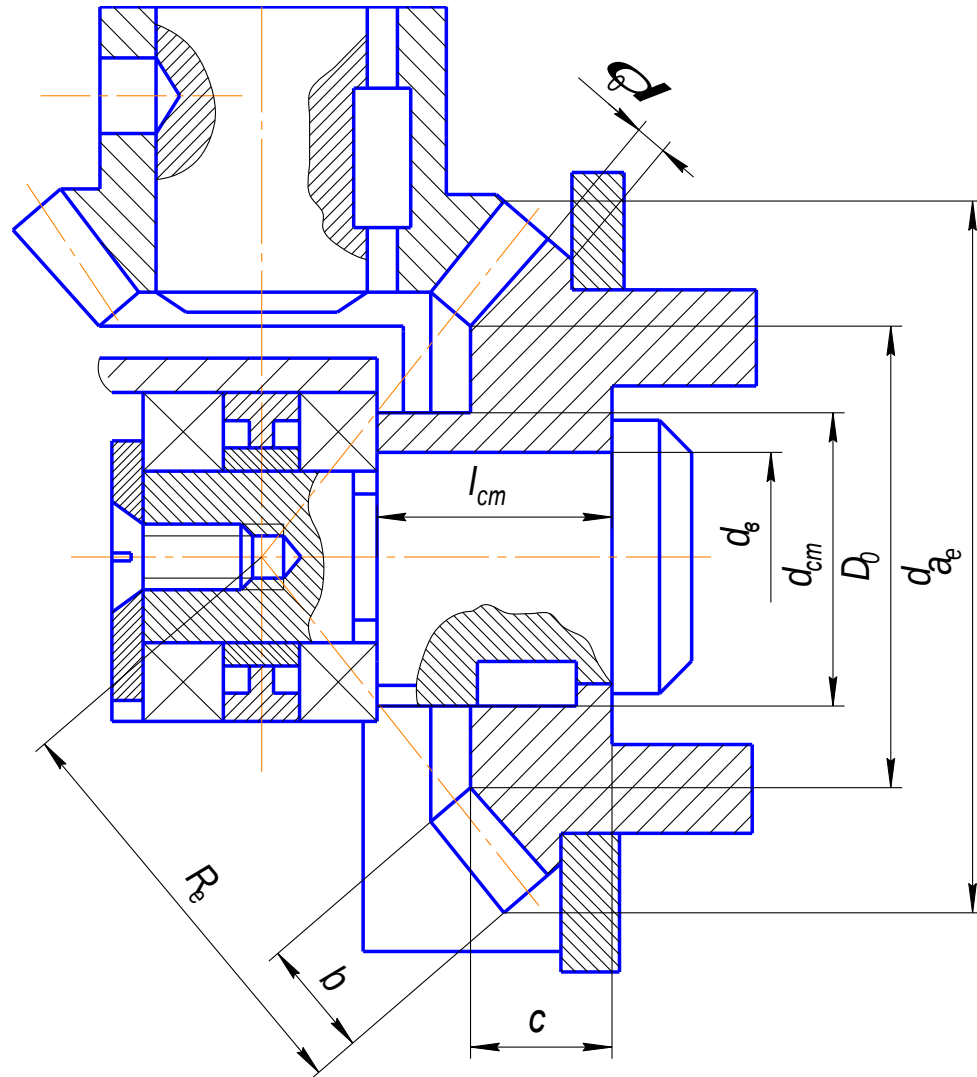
Конструкція конічної передачі вертикальної шпиндельної бабки фрезерного верстата.
